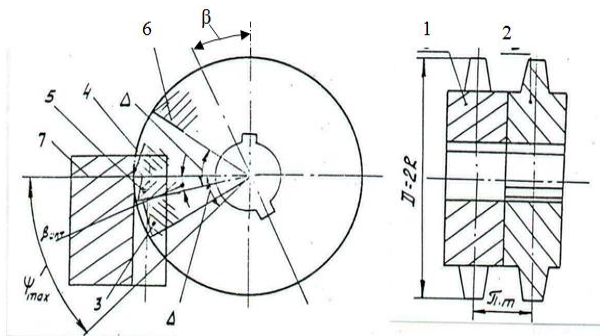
Синтез параметров операции зубонарезания реек спаренными дисковыми фрезами: 1 -спаренная дисковая зуборезная фреза левая; 2 -спаренная дисковая зуборезная фреза правая; 3, 4 -смежные режущие зубья фрезы левой; 5, 6 -смежные режущие зубья фрезы правой; 7 – обрабатываемая зубчатая рейка
